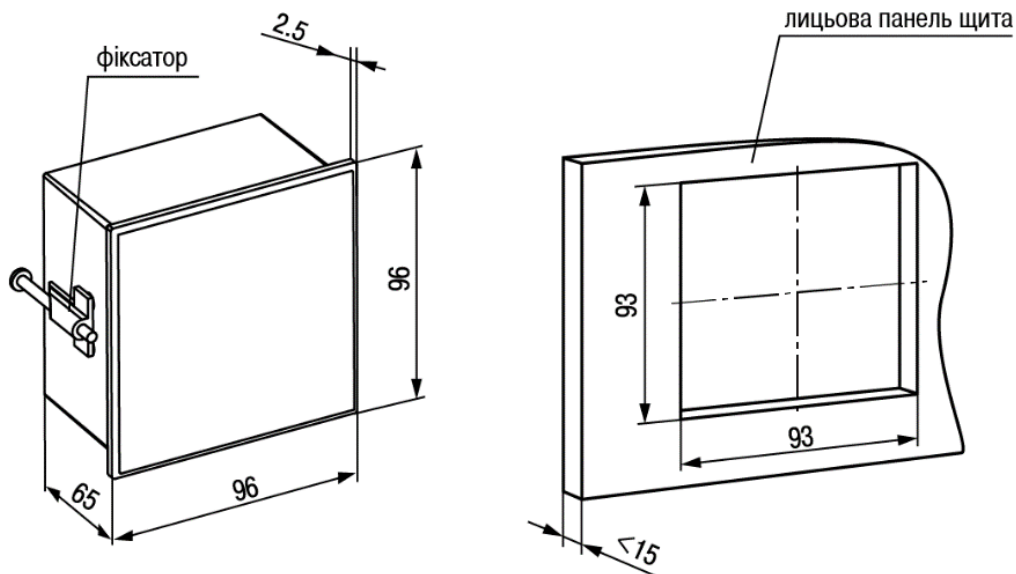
Габаритні розміри корпусу Щ1
